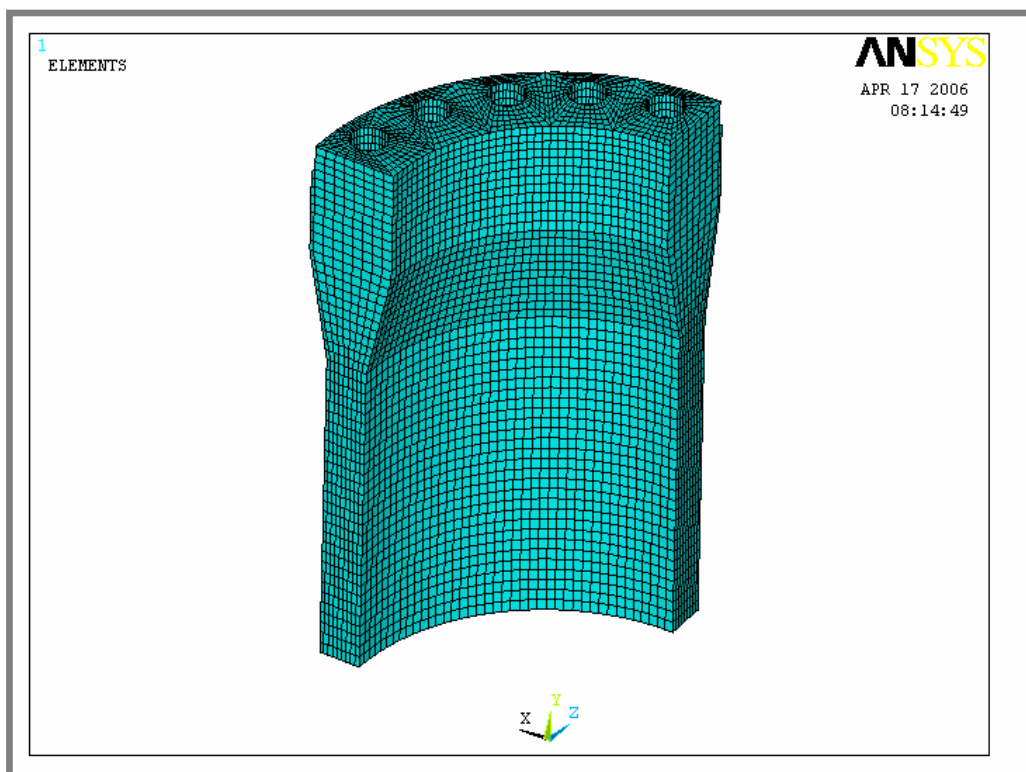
Výsledek operace rotace kolem osy
